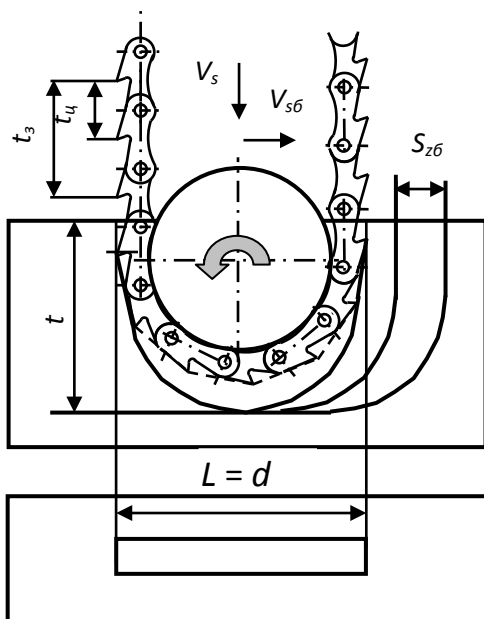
Схема цепного фрезерования (долбления) гнезда
